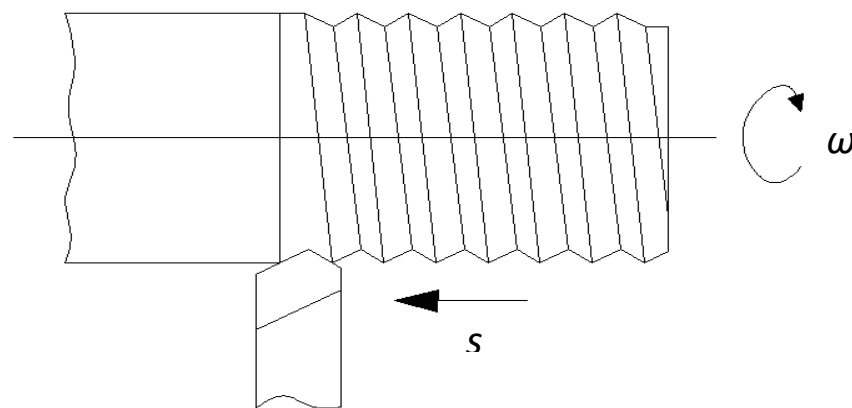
Схема утворення залишкового гребінця в процесі оброблення
